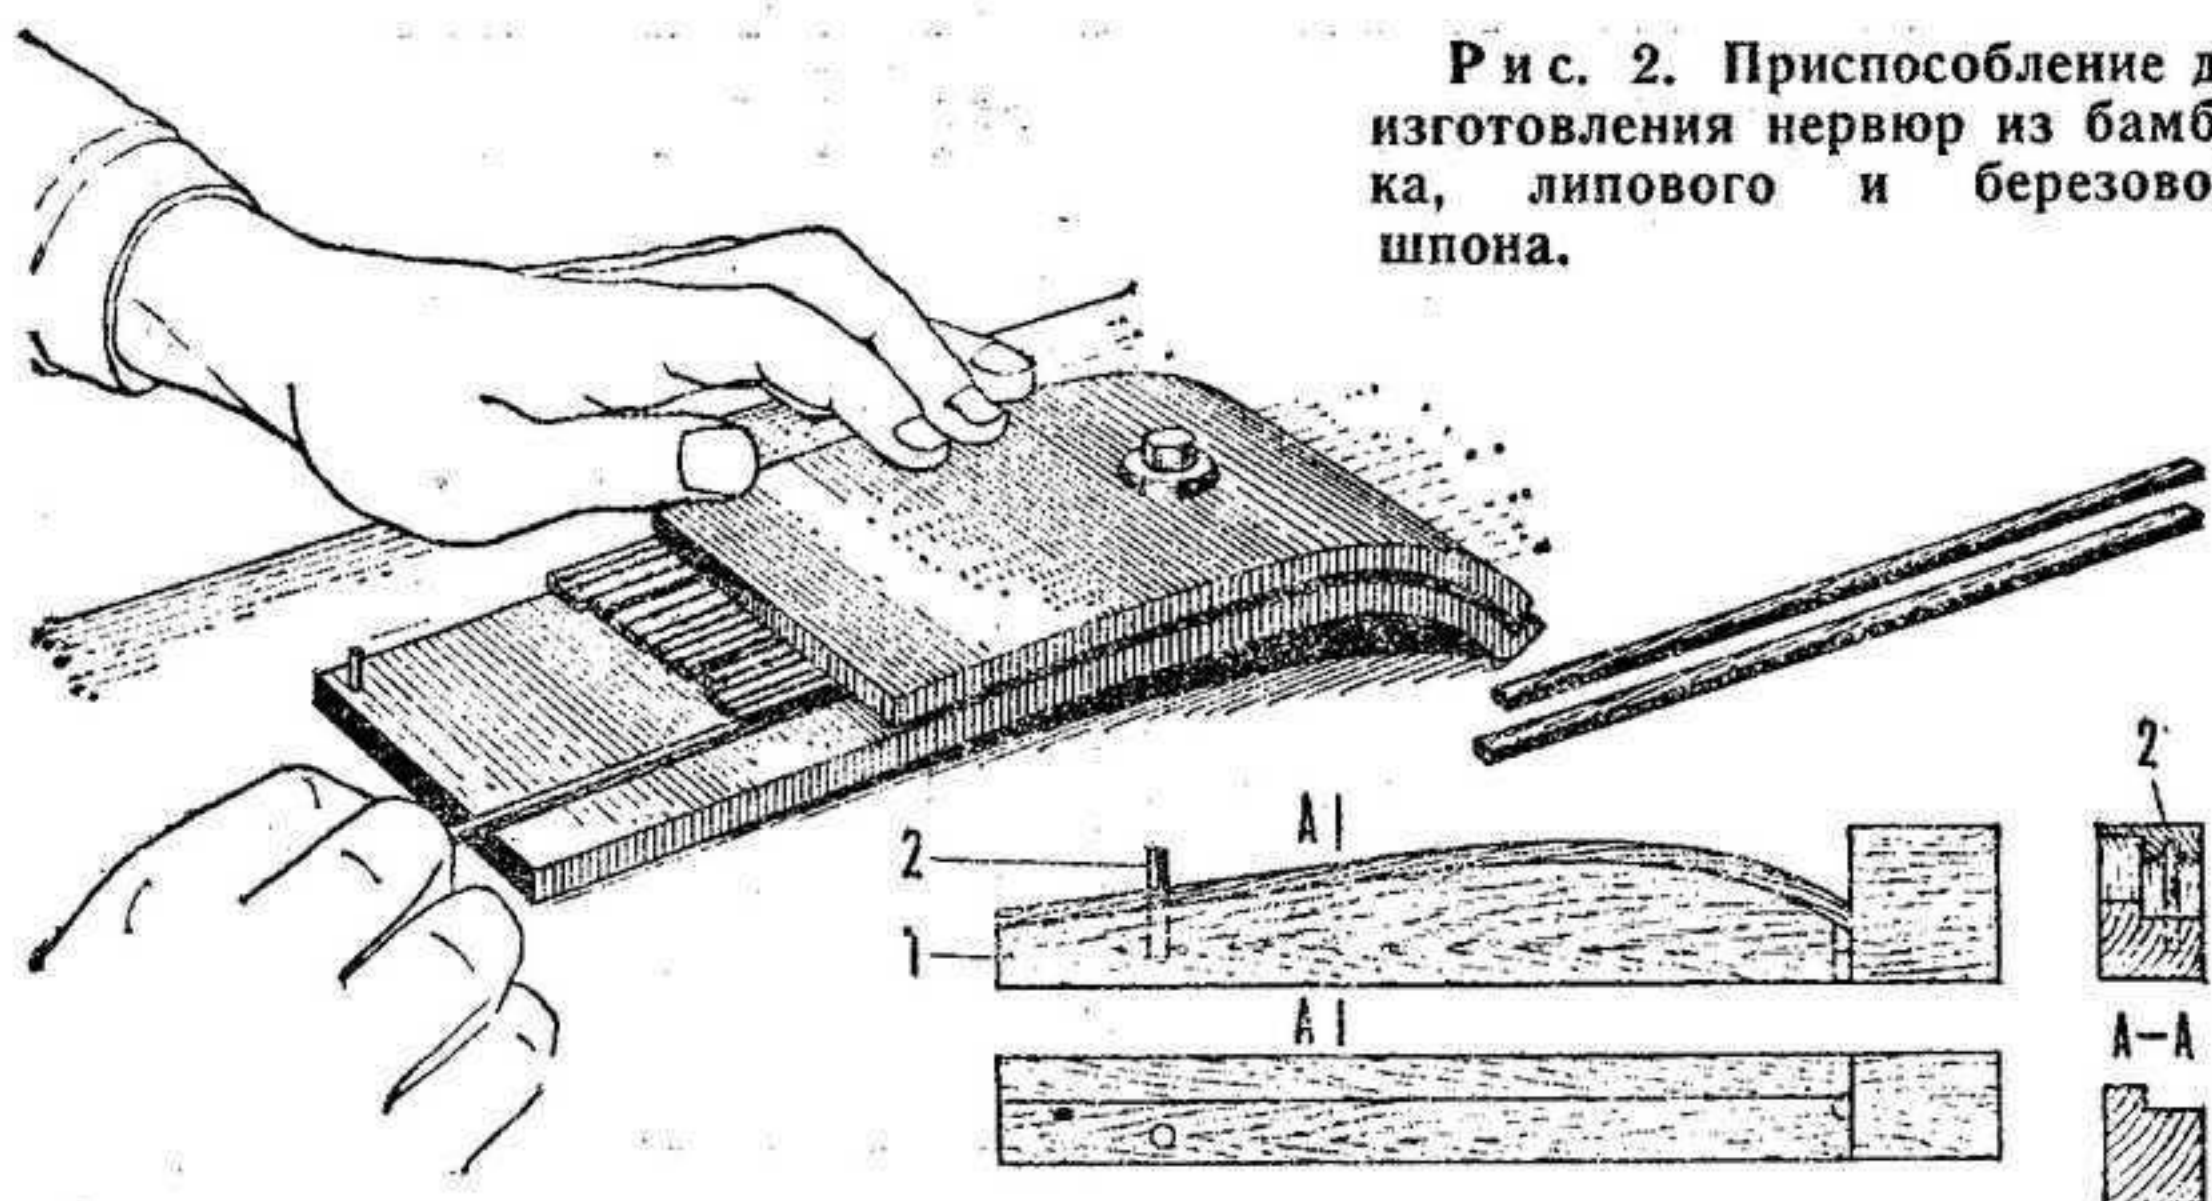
Приспособление для изготовления нервюр из бамбука, липового и березового шпона.
